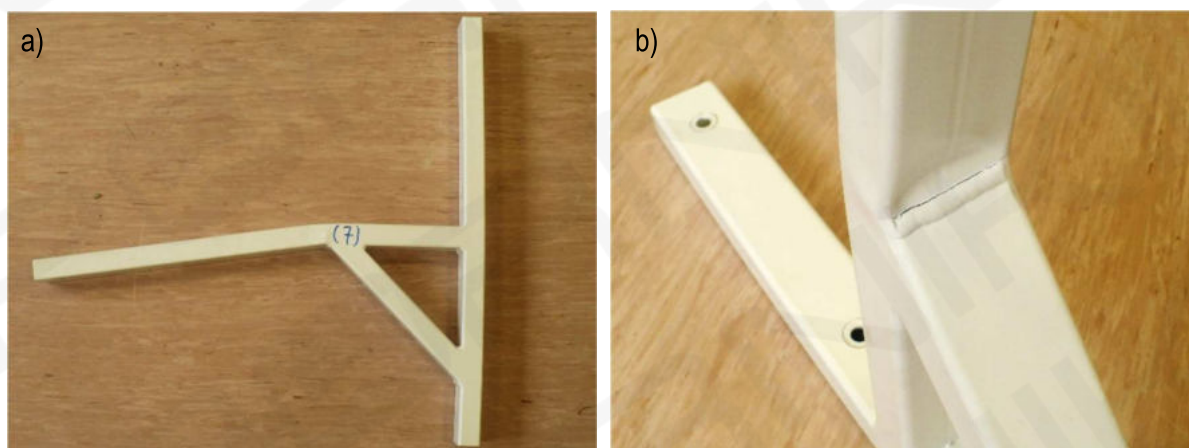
Widok zniszczonego elementu P4: a) widok ogólny, b) miejsce zniszczenia
